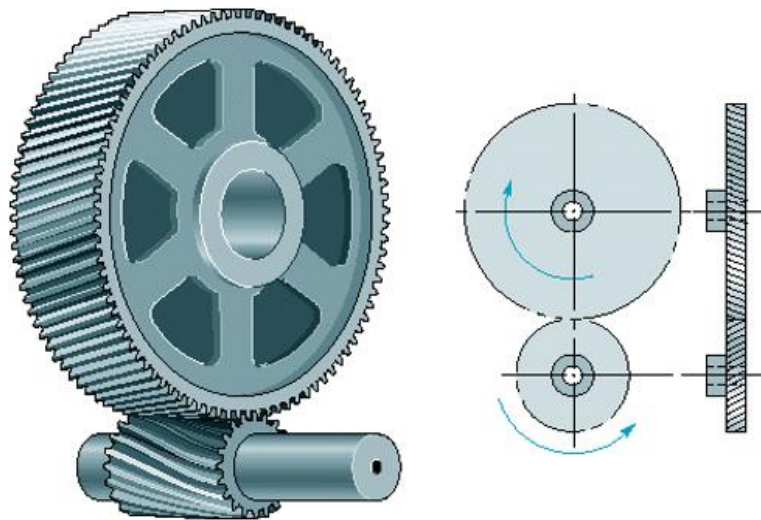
Engranaje cilíndrico helicoidal [25]
